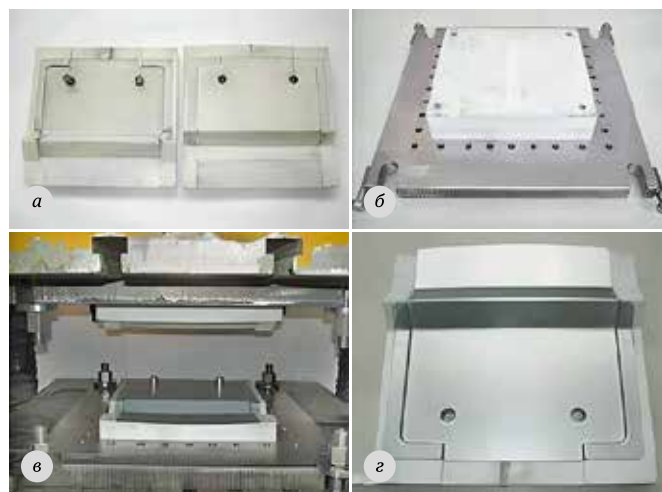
Пример штампа для формовки детали из листового металла: а – верхний и нижний штампы; б – штампы в сборе; в – штамп в рабочей зоне пресса; г – штампованная деталь в нижнем штампе [9]
